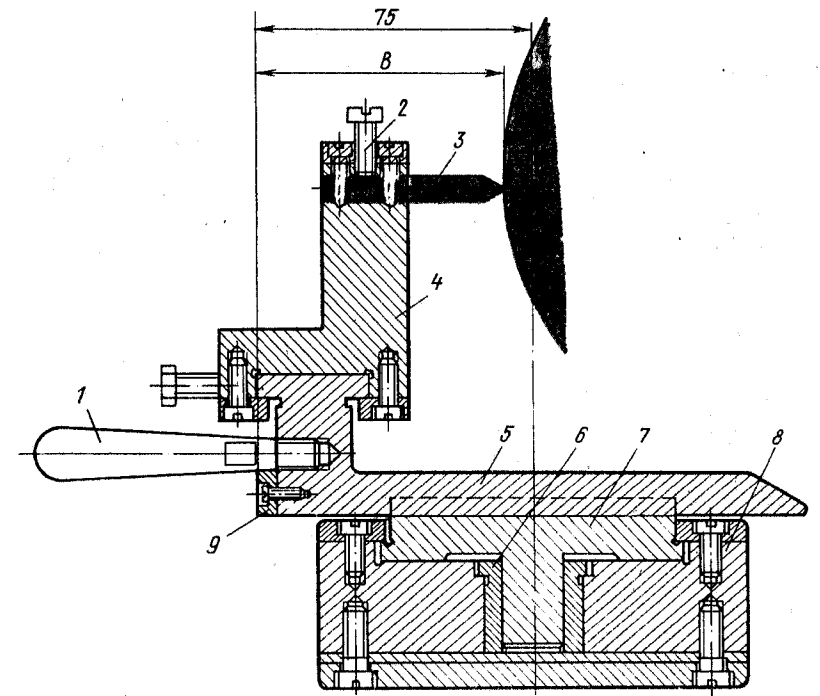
Приспособление для правки рабочей поверхности круга по дугам окружности
